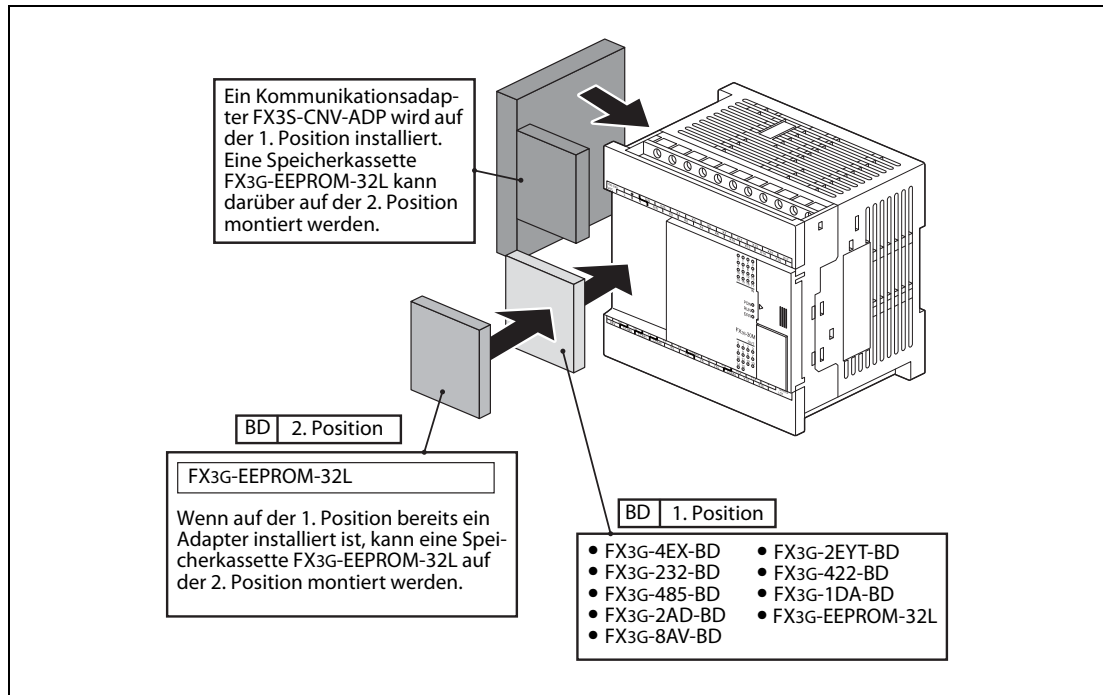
Montagepositionen für Module in einem FX3S-Grundgerät
